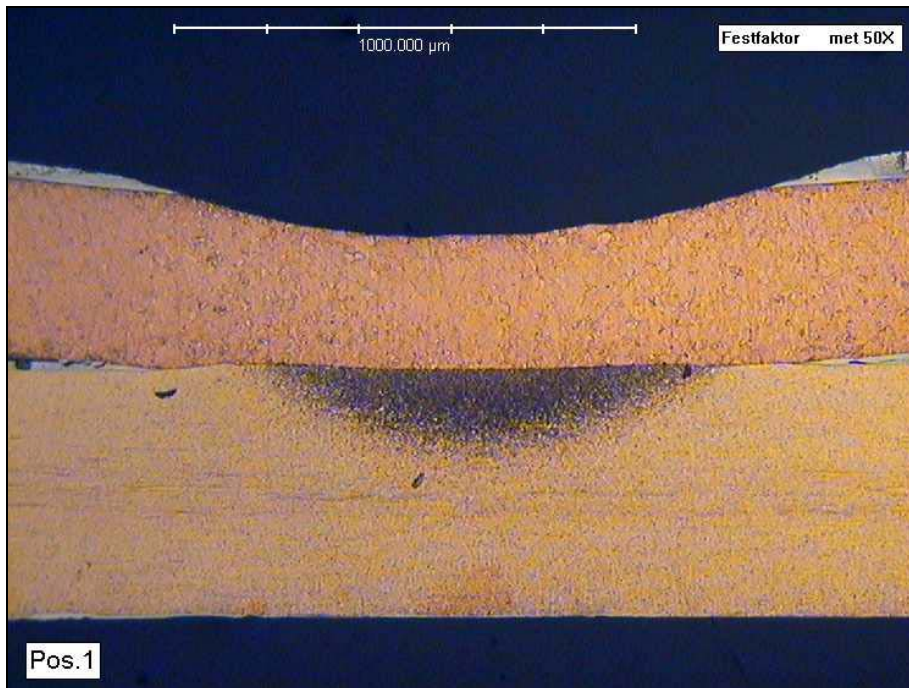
Schliffbild. Punktschweißverbindung.
